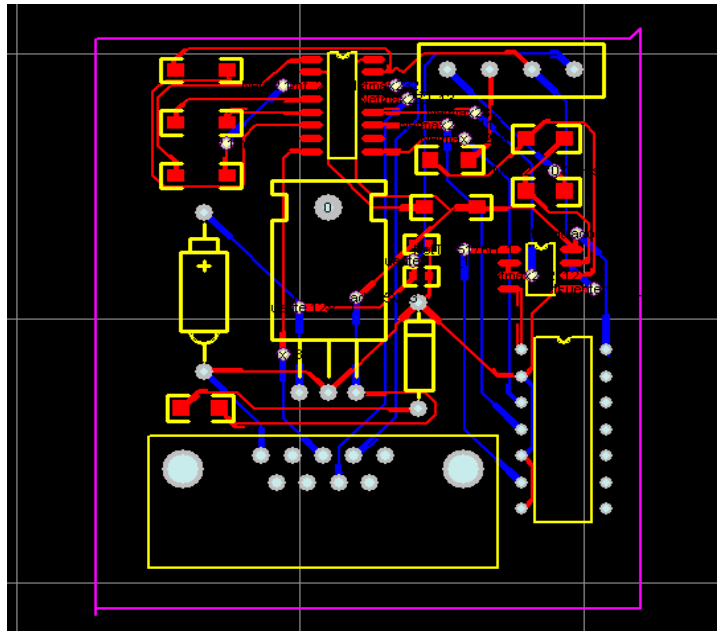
PCB de la tarjeta de conversión RS232-RS485.
